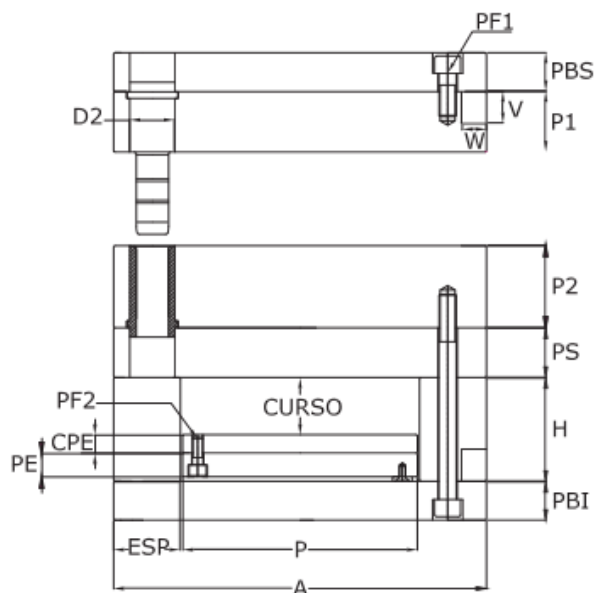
Montaje estándar para un molde de la marca Polimold.
